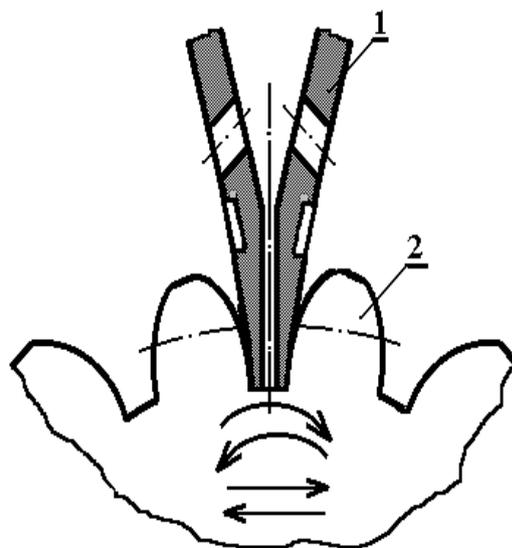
Шлифование зубьев тарельчатыми кругами
